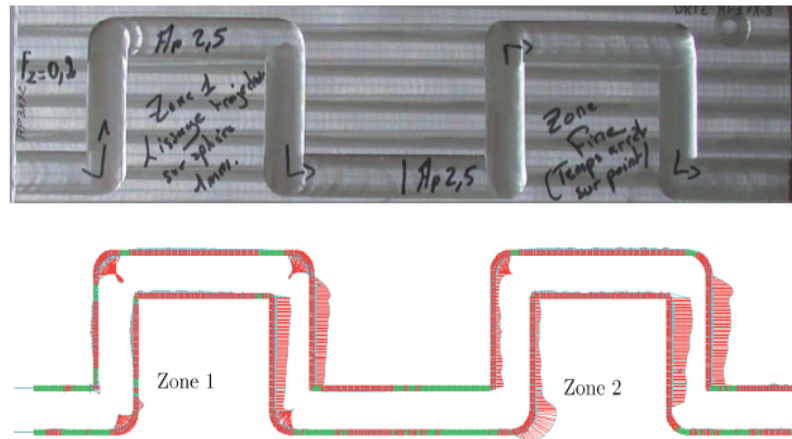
Essais d'usinage avec le robot ABB IRB 6600 [Dumas, 2011].
